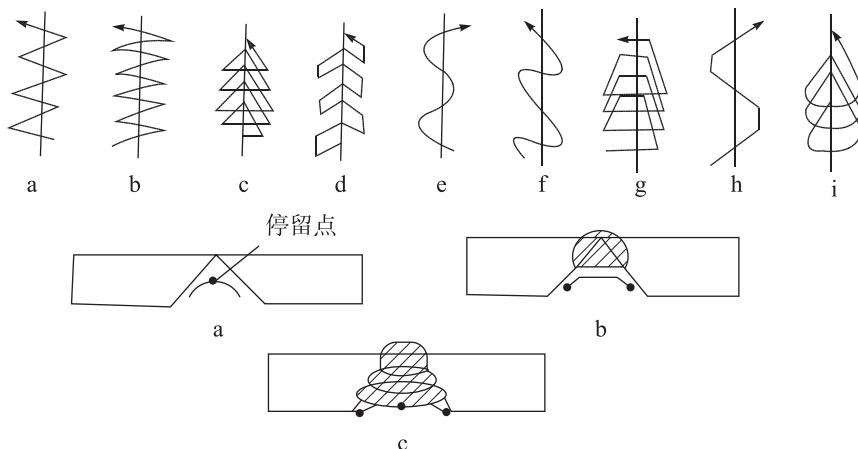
焊枪摆动方式和焊枪停留点示意图
